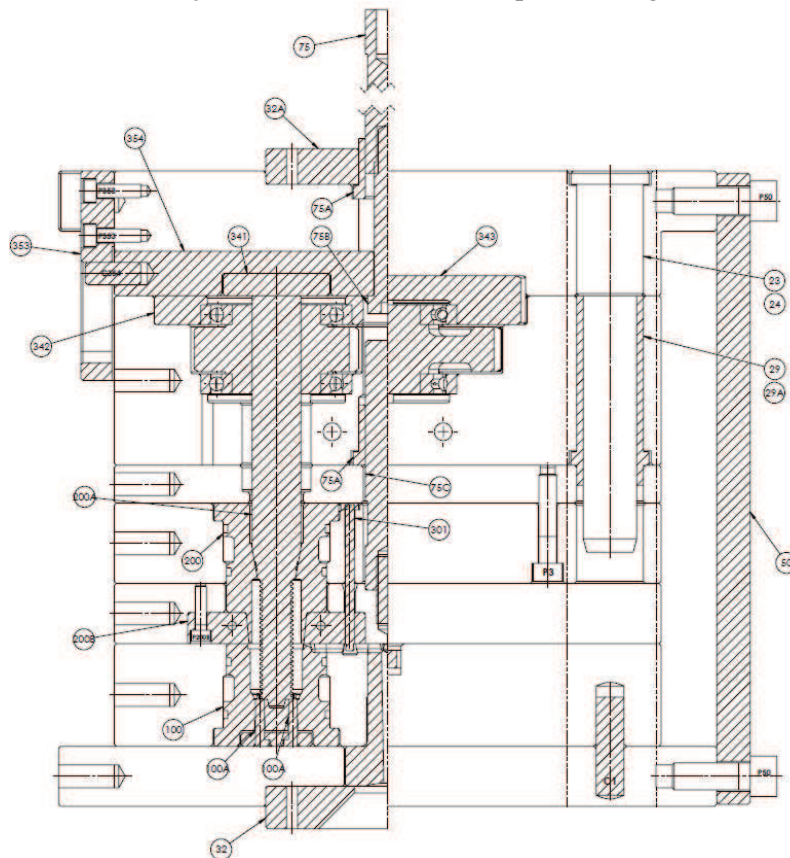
Molde de injeção com indicação dos vários componentes do molde 828 (vista em corte: seção B-B (desenho 2D final para montagem)).
